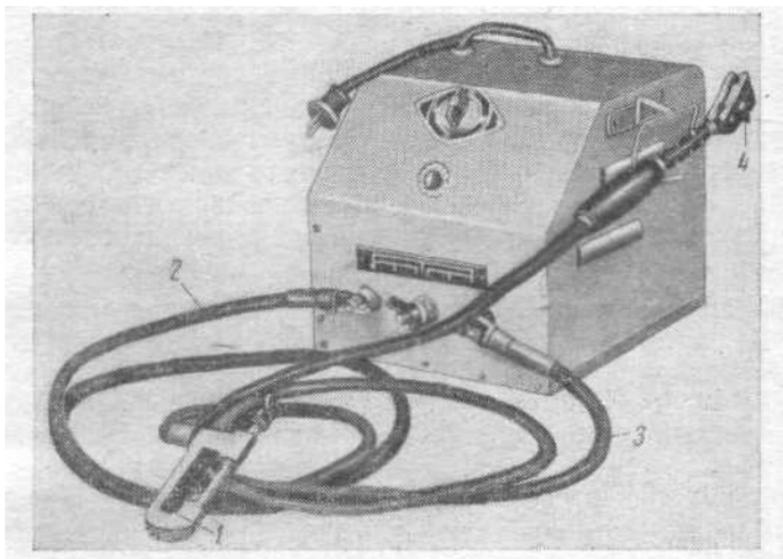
Аппарат НИИАТа для сварки-пайки тонколистового материала
